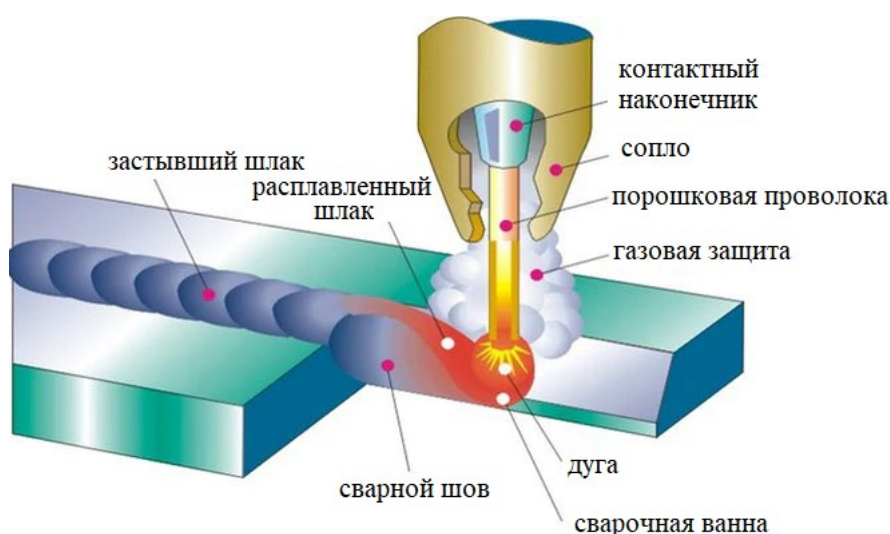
Схема выполнения сварки самозащитной порошковой проволокой
